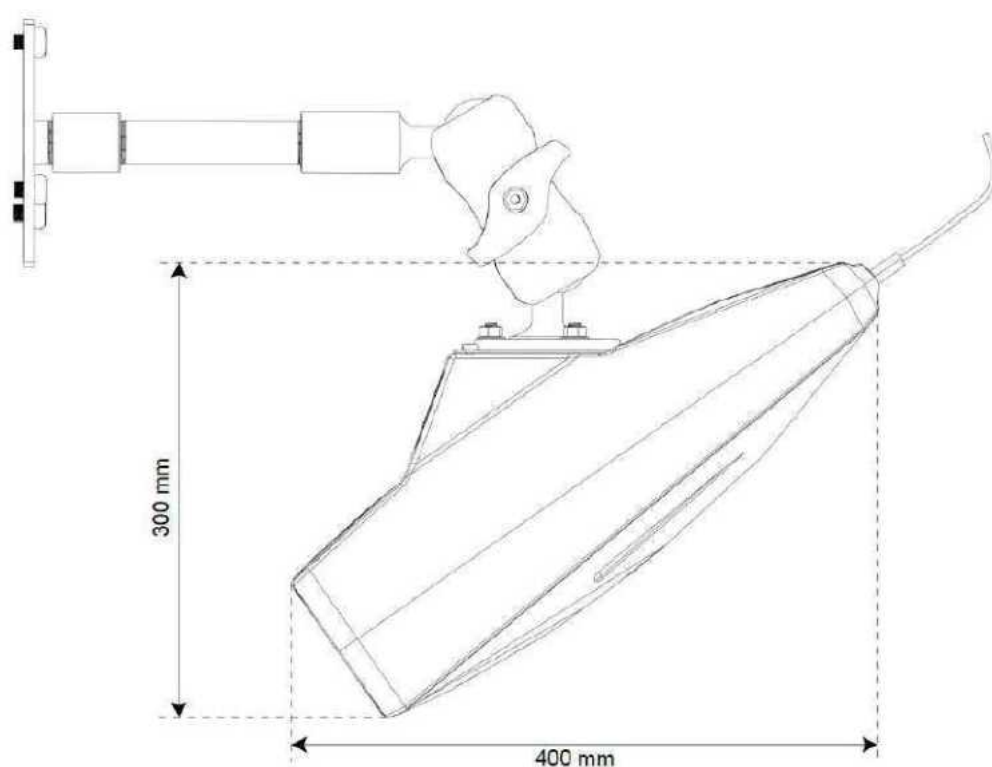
Vista lateral de las dimensiones del sensor RAVEN EYE según se ha instalado
